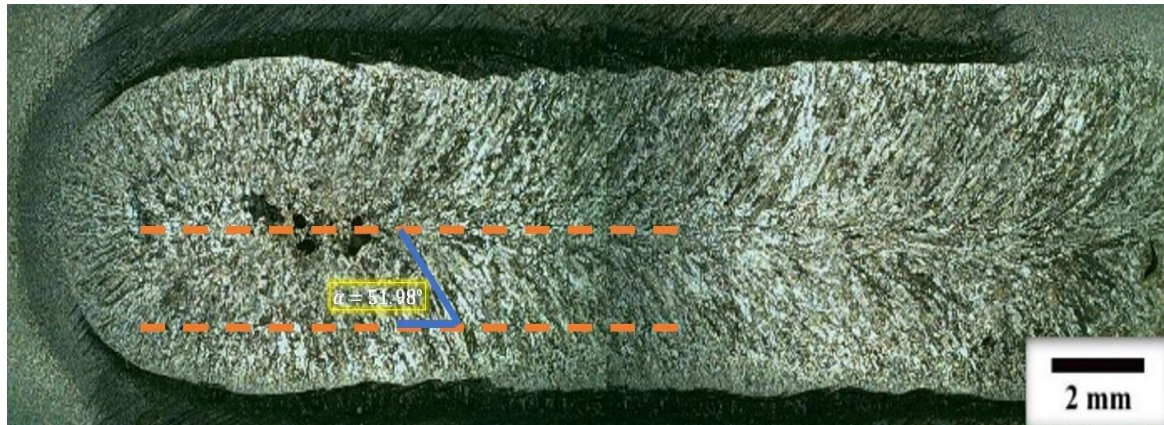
Macrografía del cordón de soldadura para calcular el ángulo con respecto al crecimiento de grano.
